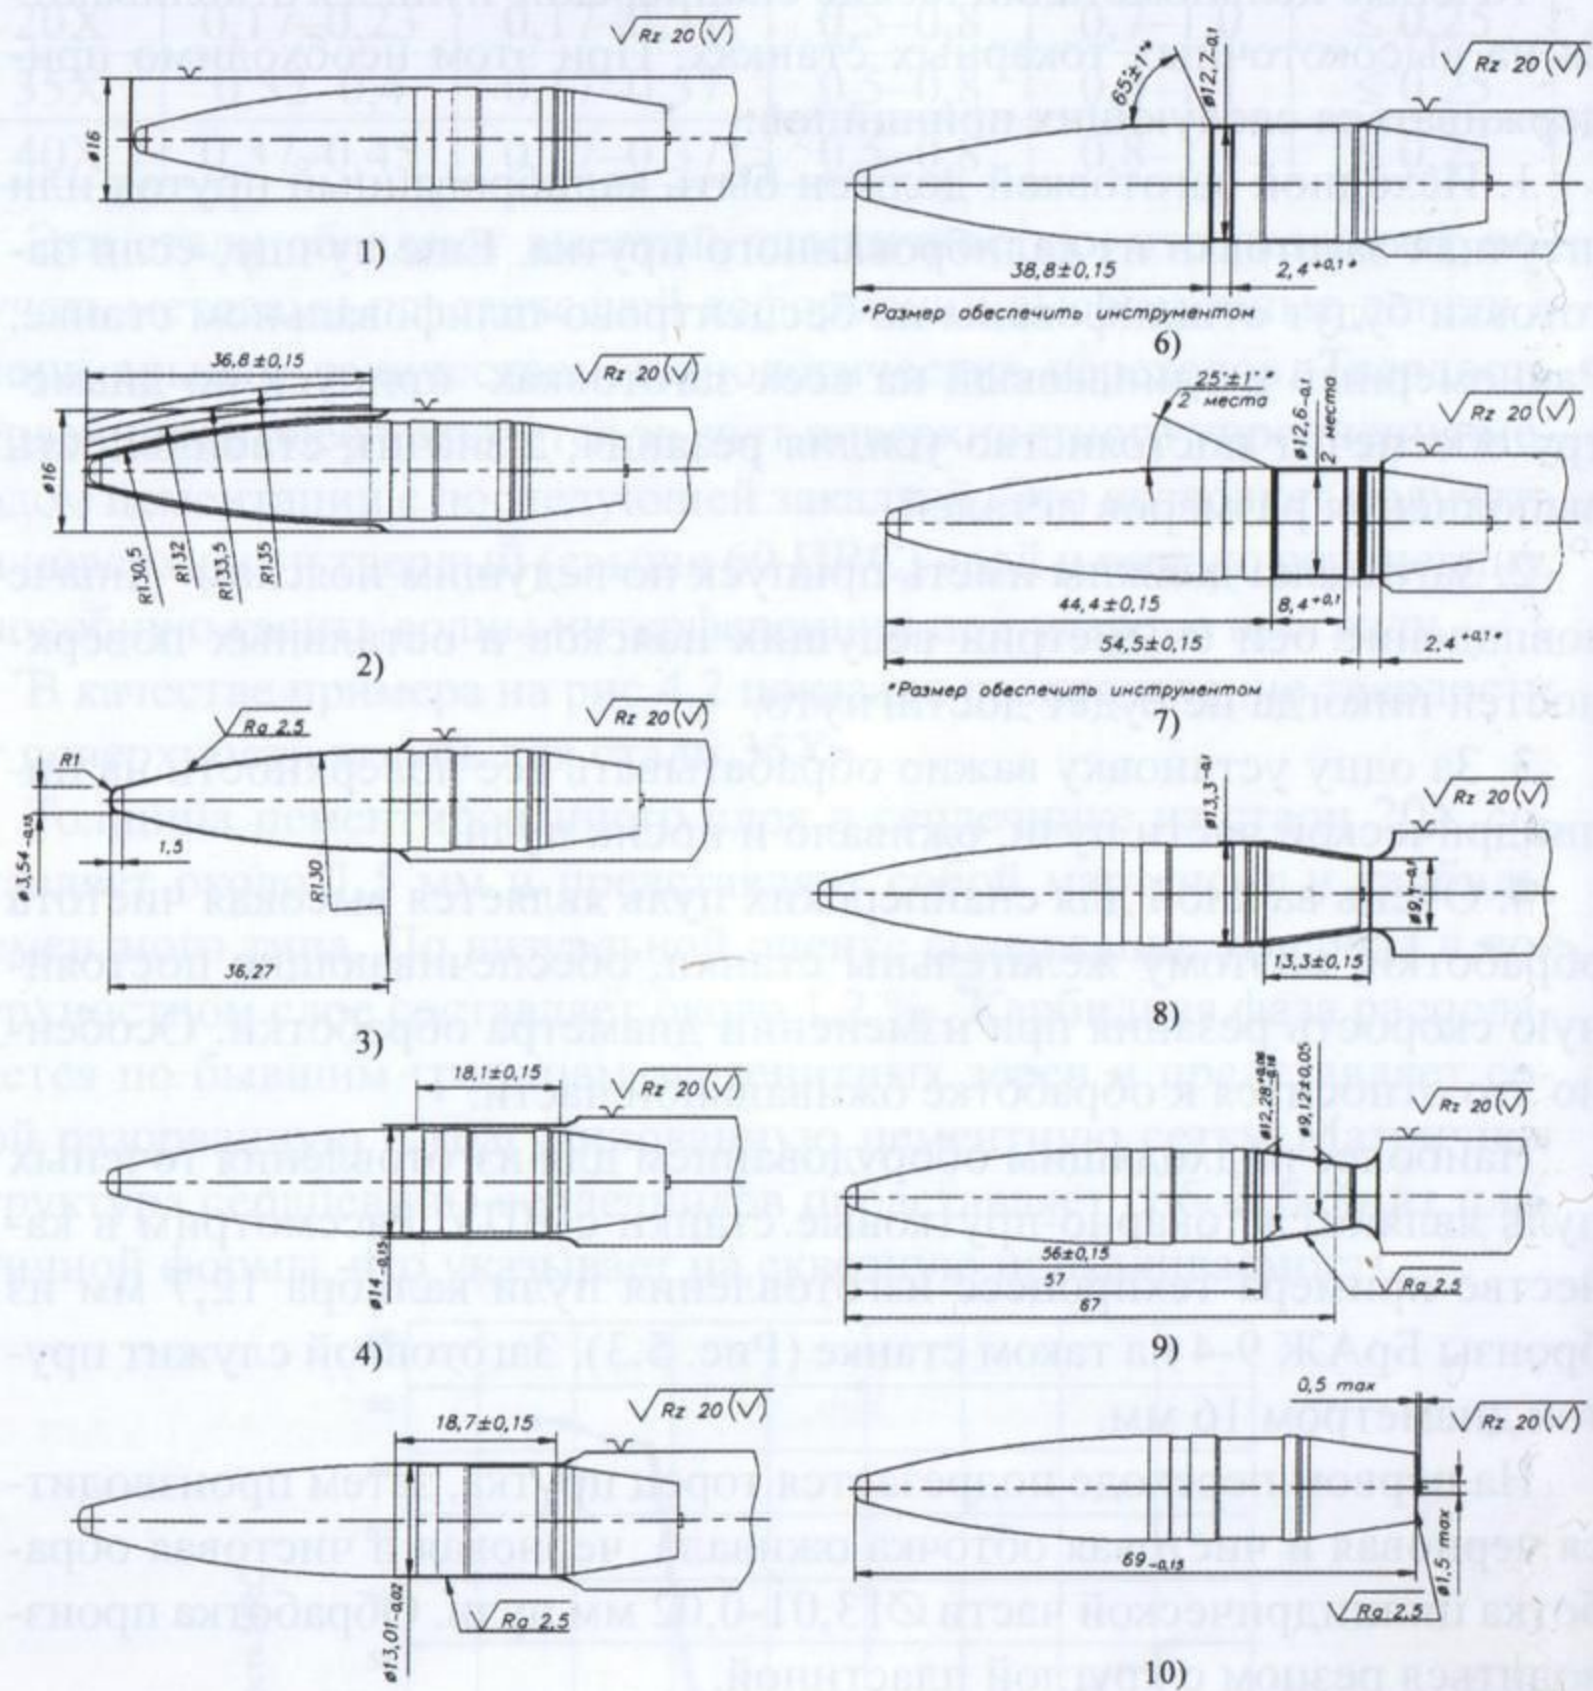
Техпроцесс изготовления пули калибра 12,7 мм на станке с ЧПУ
